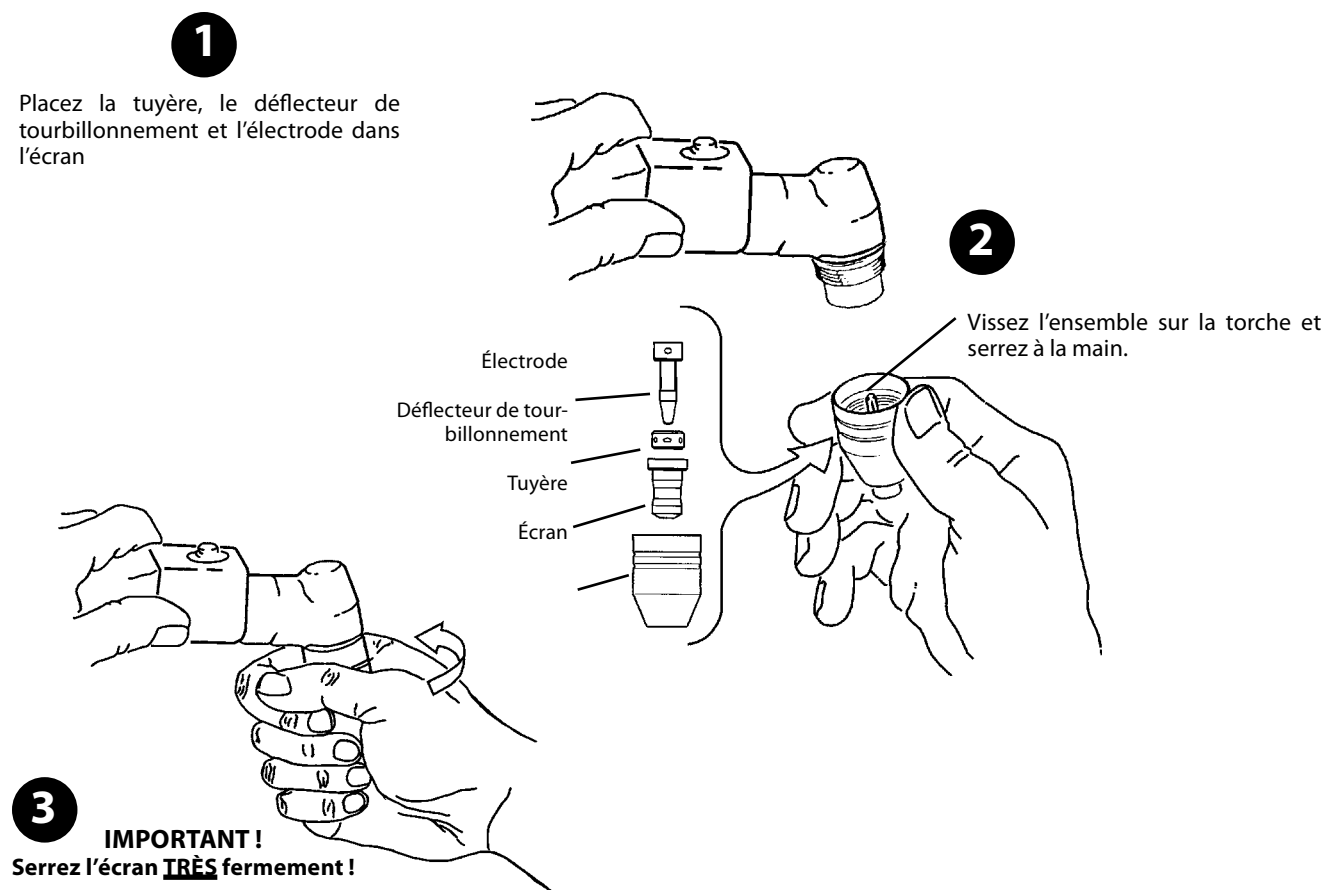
Assemblage des pièces de l'extrémité avant de la torche PT-27
